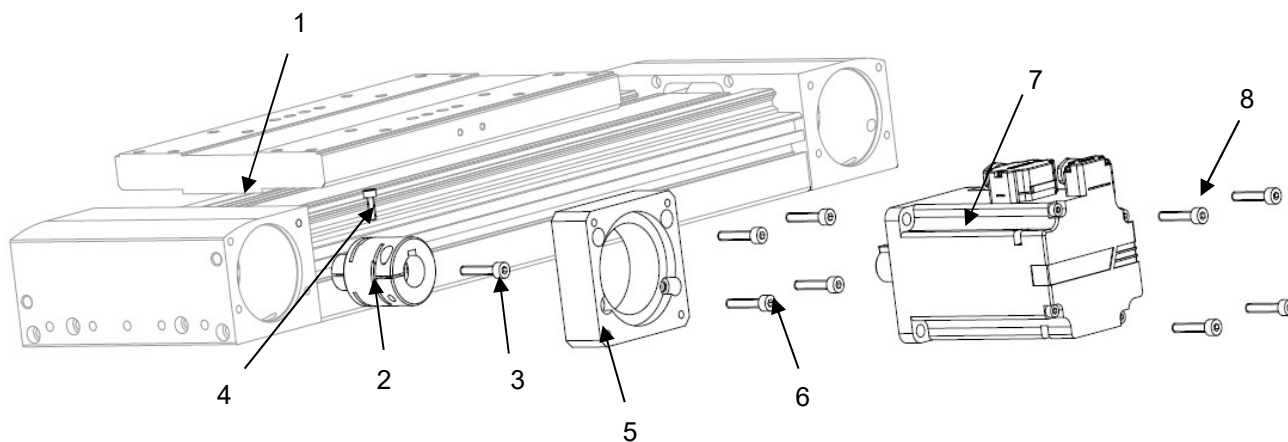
Установка двигателя с помощью монтажного комплекта модели AM-EGT
